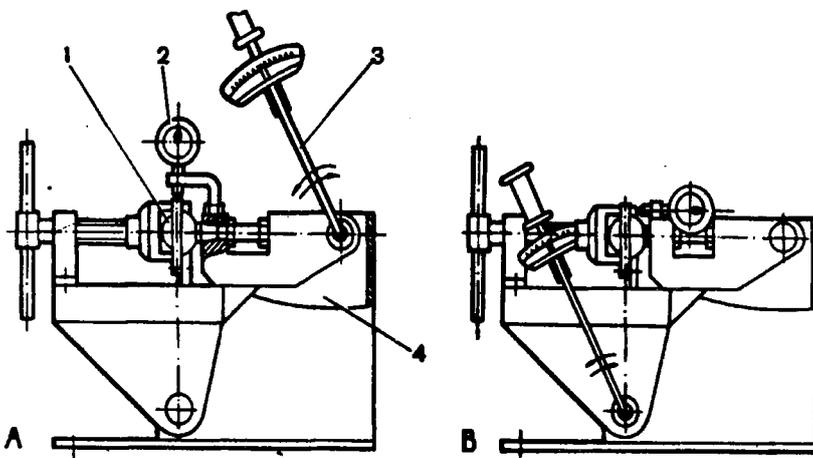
Проверка верхнего шарового шарнира на приспособлении 02.8701.9502: 1 - шаровой шарнир; 2 - индикатор; 3 - динамометрический ключ; 4 - приспособление 02.8701.9502; А - схема проверки радиального зазора; В - схема проверки осевого зазора
